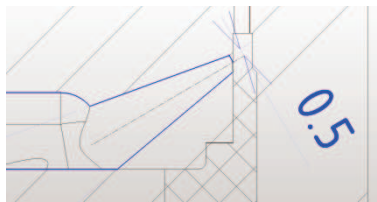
Pormenor do ataque submarino em corte (retirado do 2D).
